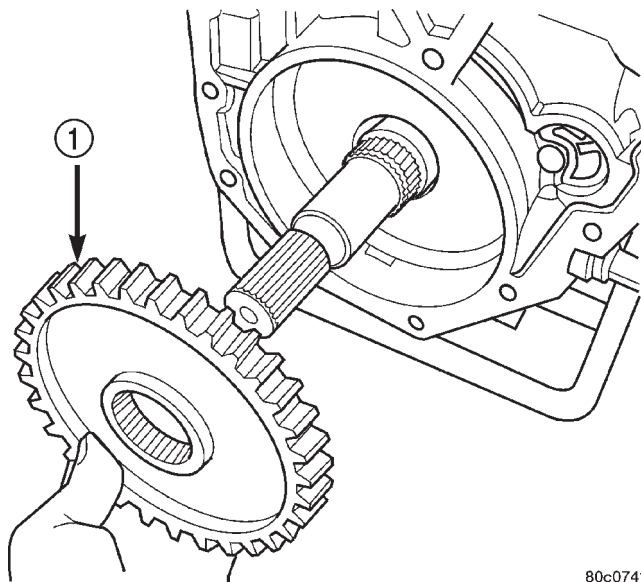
Desmontaje del engranaje de calce de estacionamiento
